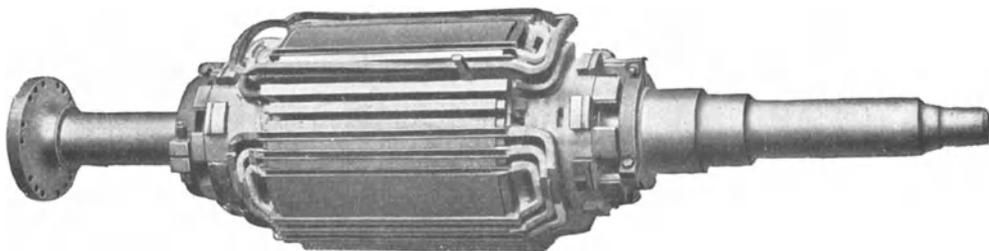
Halbfertiger Läufer einer Turbomaschine.
